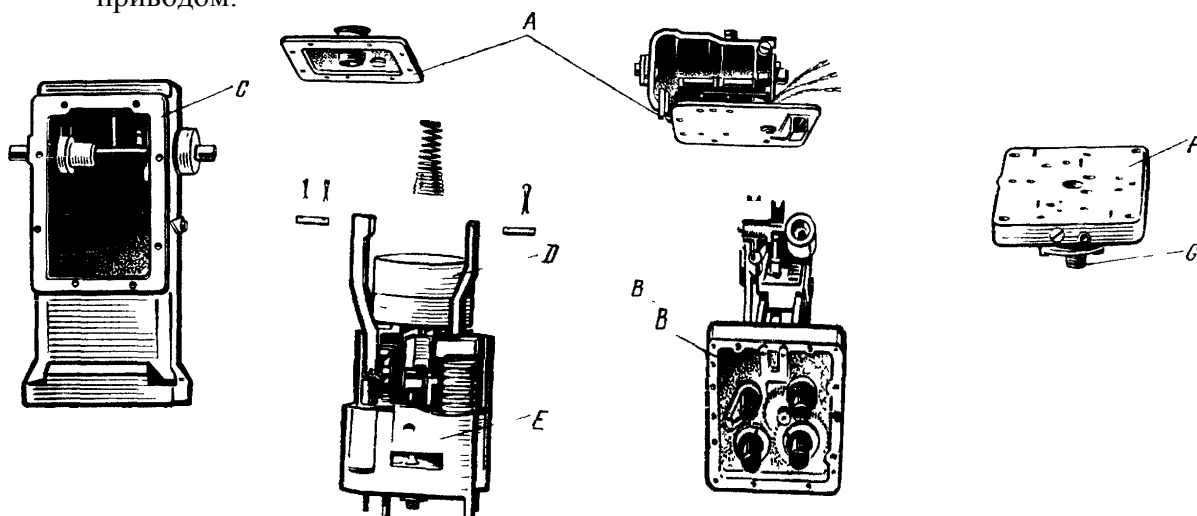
А— узел верхней крышки (без двигателя и с синхронизирующим двигателем), В — узел панели управления; С—узел корпуса; D—узел чувствительного элемента; E—узел регулирования; F—узел основания; G — узел приводного вала
